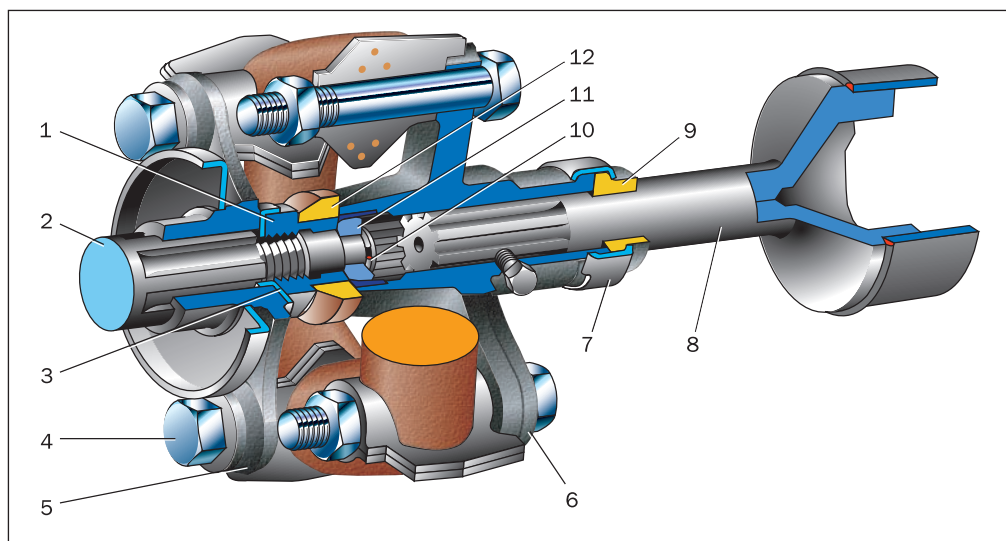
Упругая муфта Гуибо: 1 — гайка; 2 — ведомый вал коробки передач; 3 — шайба стопорная; 4 — болт (3 шт.); 5, 6 — фланцы муфты; 7 — обойма; 8 — карданный вал; 9 — сальник; 10 — стопорное кольцо; 11 — центрирующее кольцо; 12 — уплотнитель
